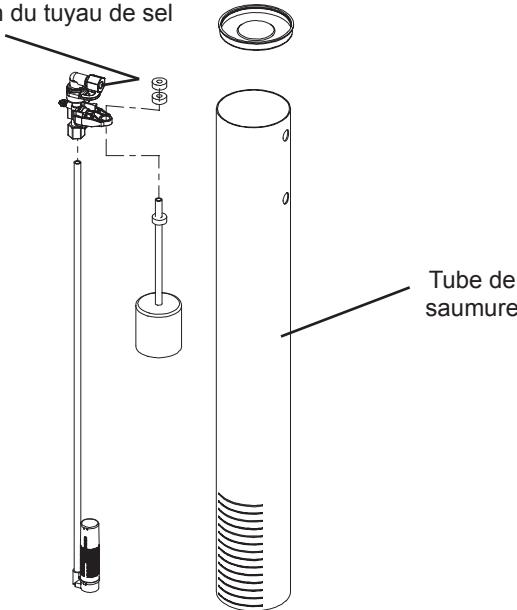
Valve de retenue du réservoir de sel et assemblage du bac à sel
